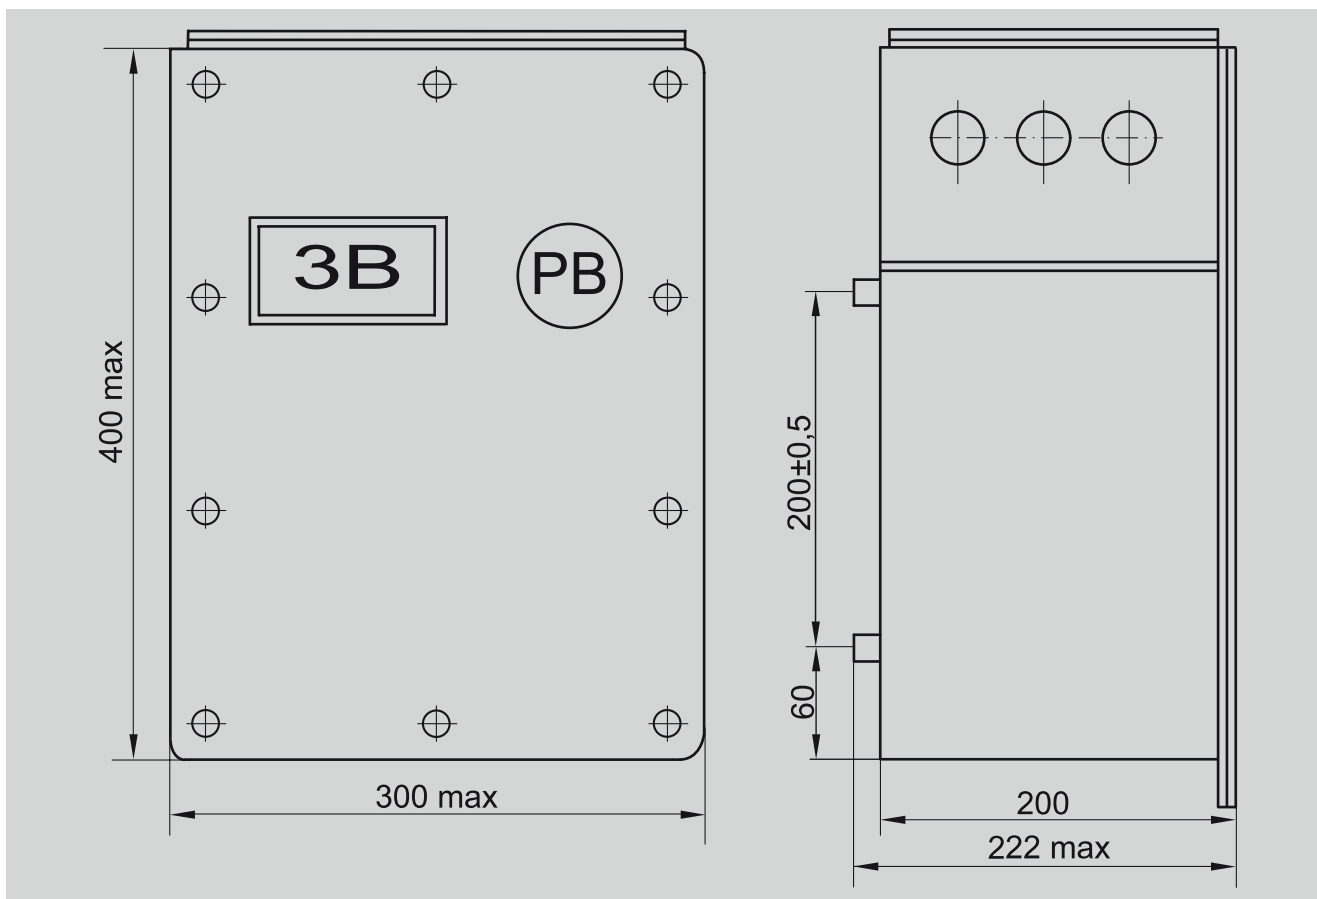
Габаритные и установочные размеры стабилизатора напряжения СНВ-2М
